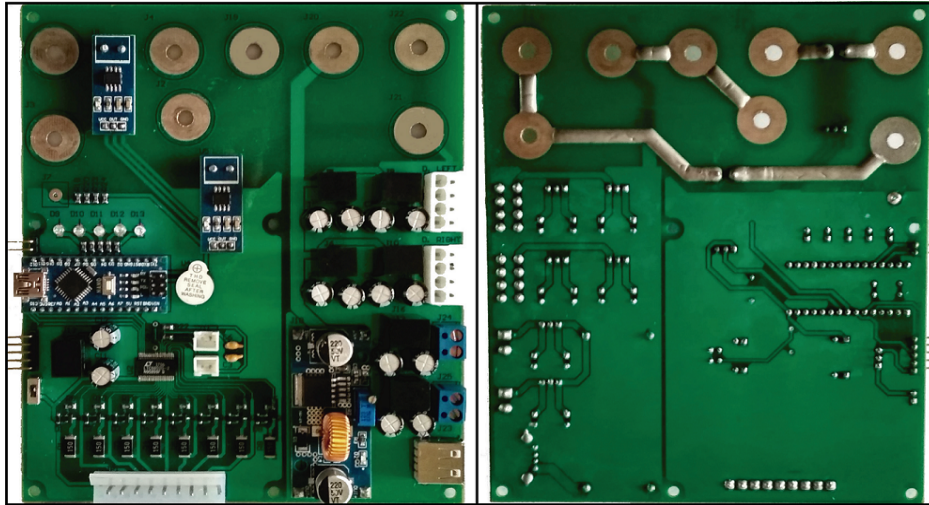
Izquierda.- Cara superior del PCB final. Derecha.- Cara inferior del PCB final.
